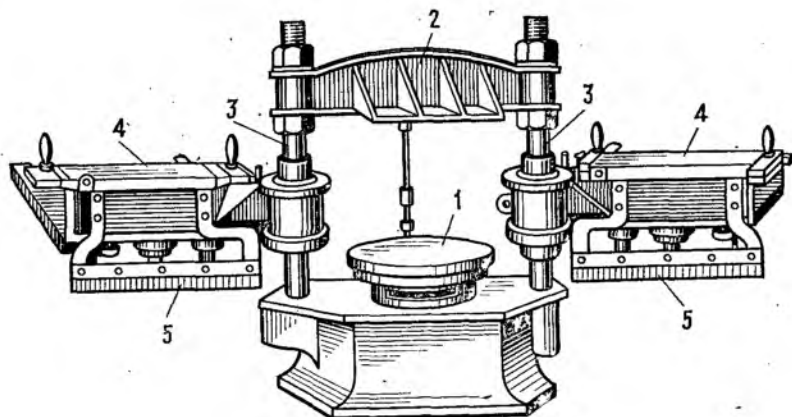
Формовочная машина с нижним прессованием мод. ПФ-3
